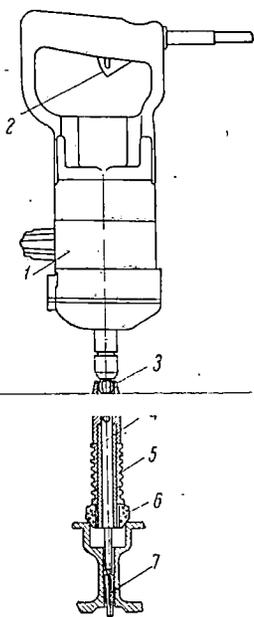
Приспособление для шлифования клапанных седел в блоке цилиндров:
